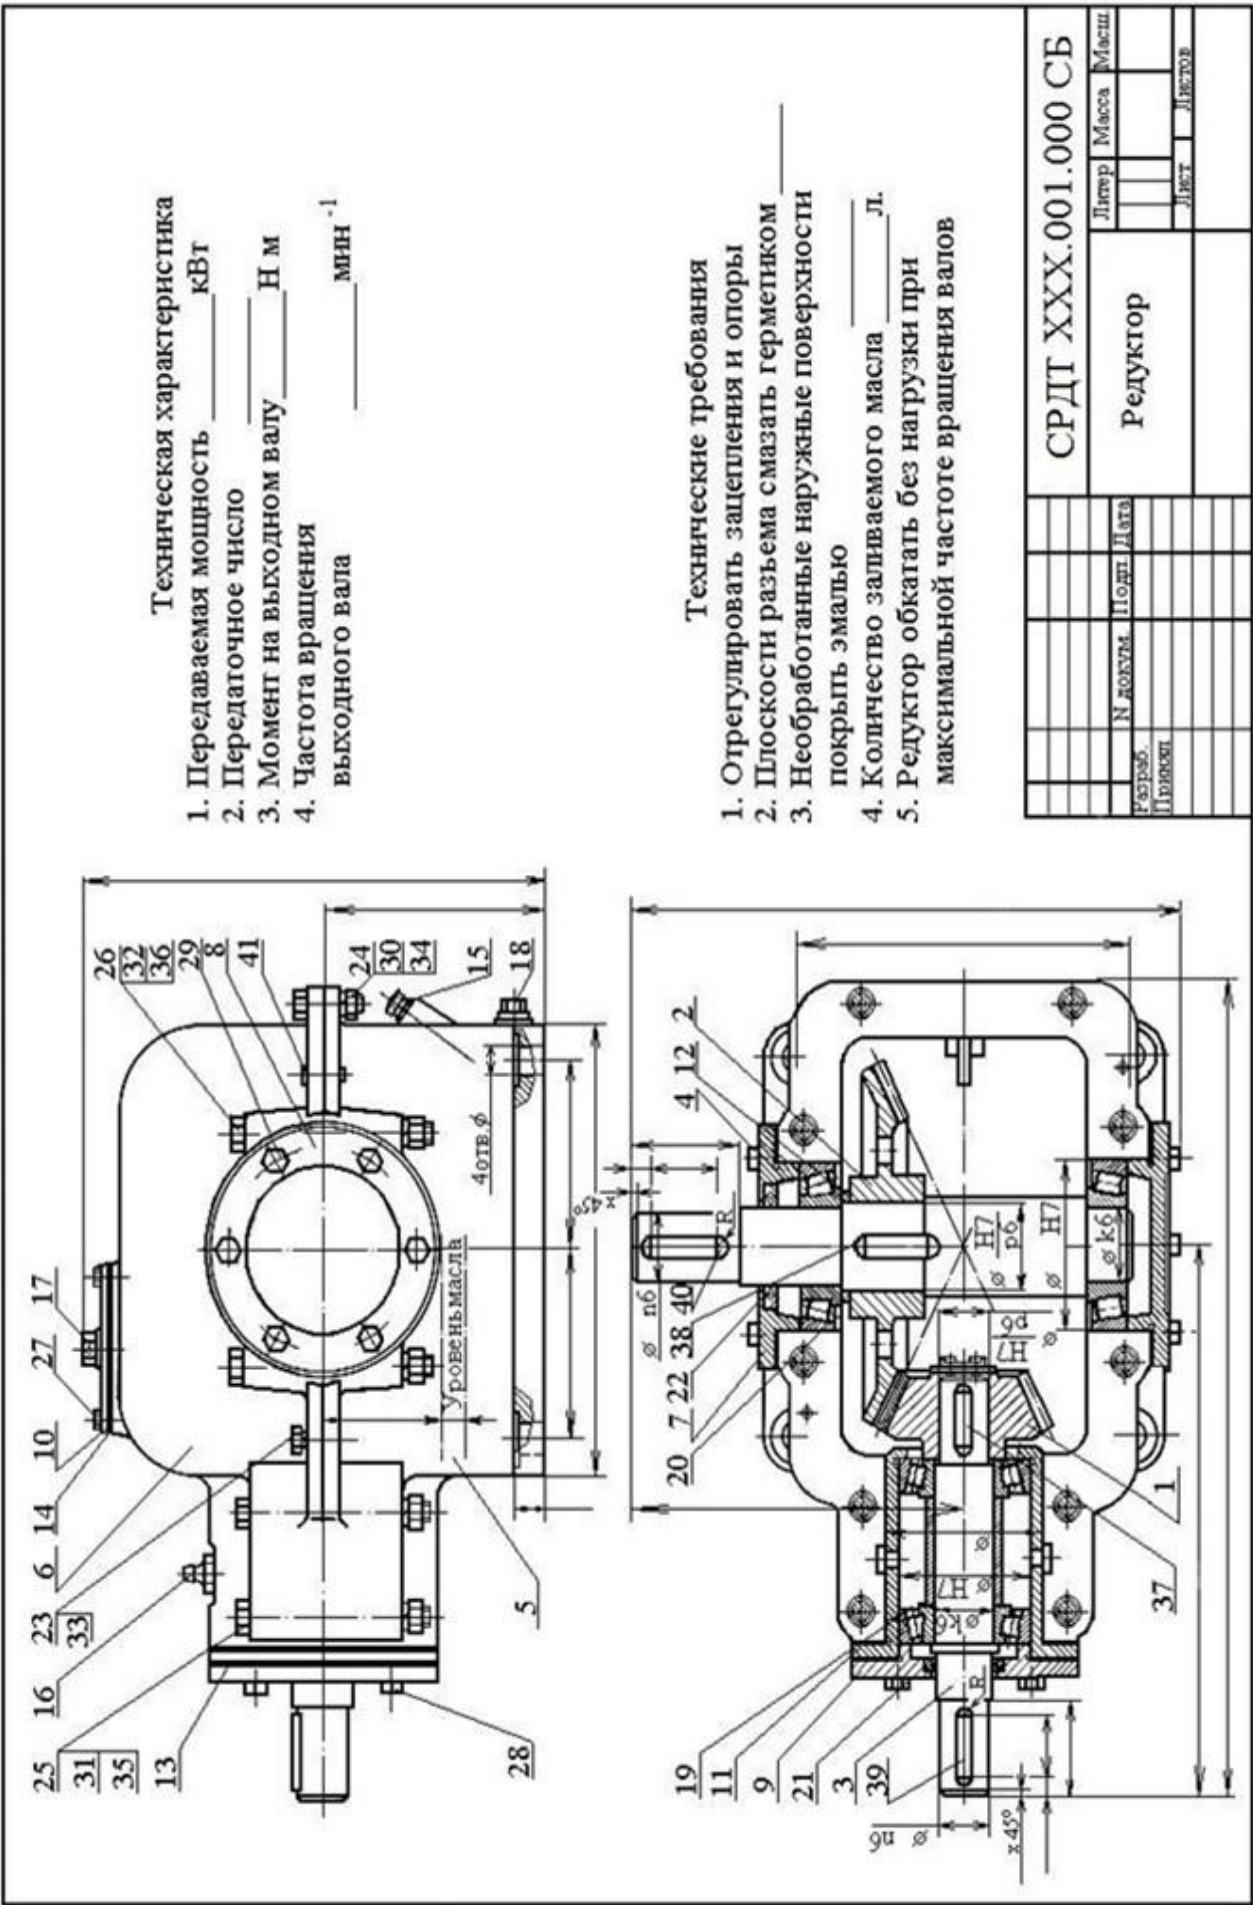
Чертеж редуктора конического одноступенчатого
